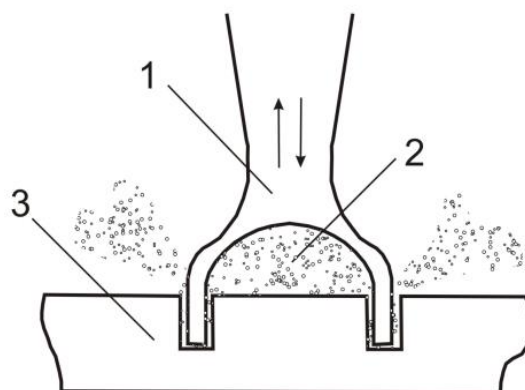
Ультразвуковая обработка материалов: 1 –ультразвуковой инструмент; 2 –абразивные зёрна; 3 –обрабатываемая деталь.
